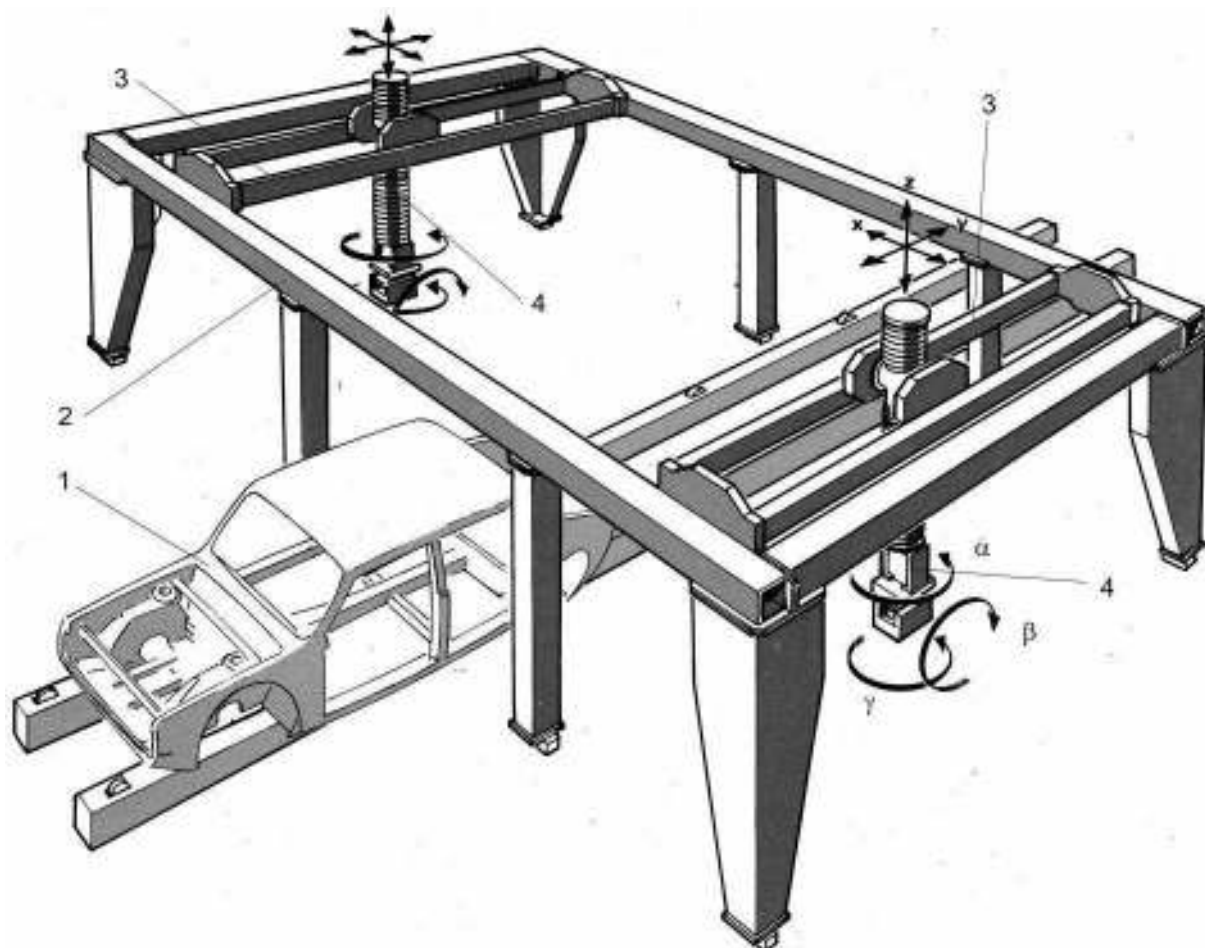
Сварочный РТК мостовой конструкции
